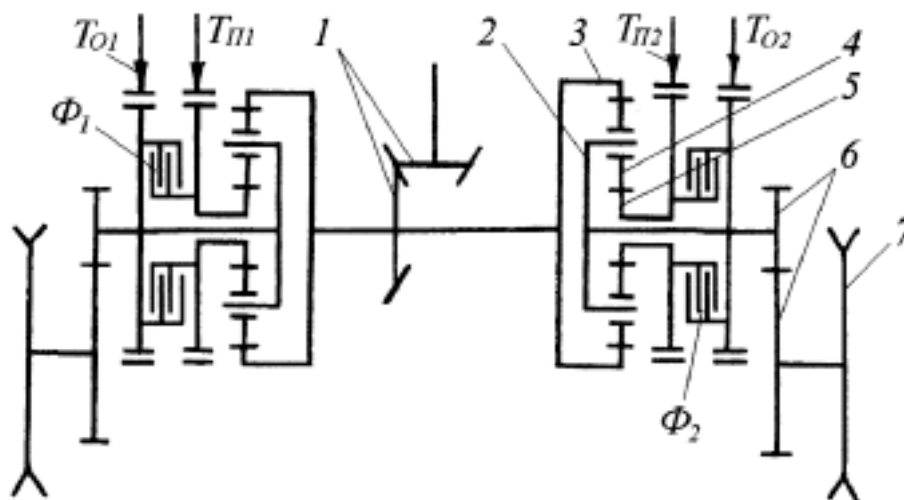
Двухступенчатый планетарный механизм поворота:
